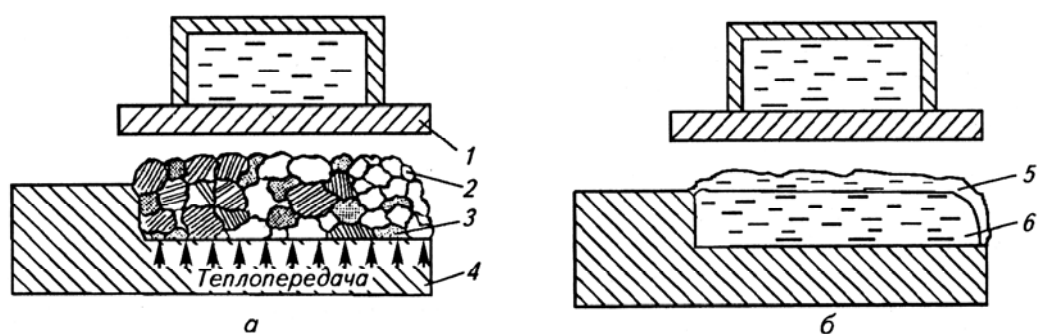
Схема способа индукционной наплавки порошкообразной шихтой: а – начало процесса; б – окончание процесса; 1 – индуктор ТВЧ; 2 – частицы наплавляемого сплава; 3 – частицы флюса; 4 – деталь; 5 – слой жидкого флюса; 6 – жидкий присадочный сплав
